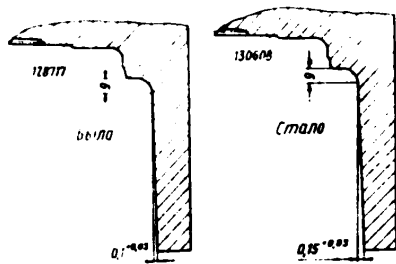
Замок гаек крепления упорного фланца и корпусов муфты включения и поршня храповика.
